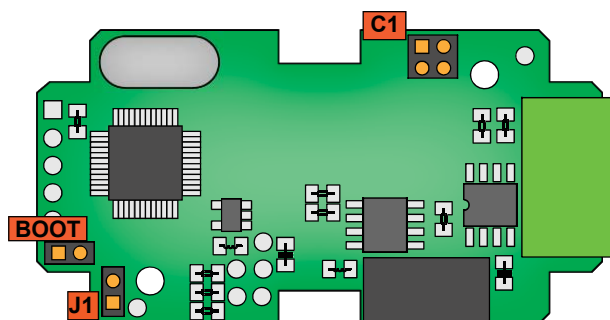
Плата USB-CAN конвертера SL-USB-10.1
